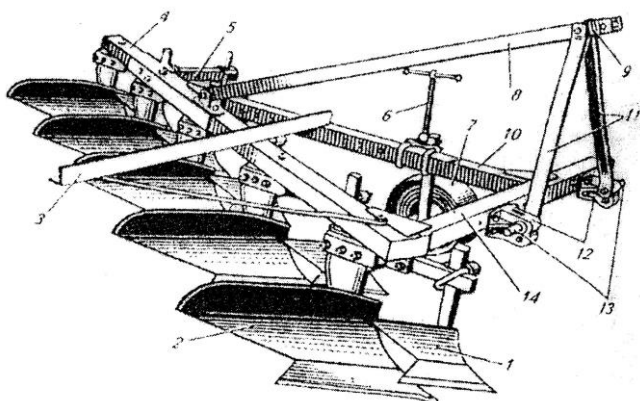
Плуг ПЛН-5-35: 1 – предплужник; 2 – корпус; 3 – прицепка для борон; 4- главная балка; 5 – кронштейн дискового ножа; 6 – винт регулирования глубины вспашки; 7 – опорное колесо; 8 – раскос; 9 – присоединительная проушина; 10 – продольная балка; 11 – подкосы навески; 12 – кронштейны присоединительных пальцев; 13– присоединительные пальцы; 14 – поперечная балка
